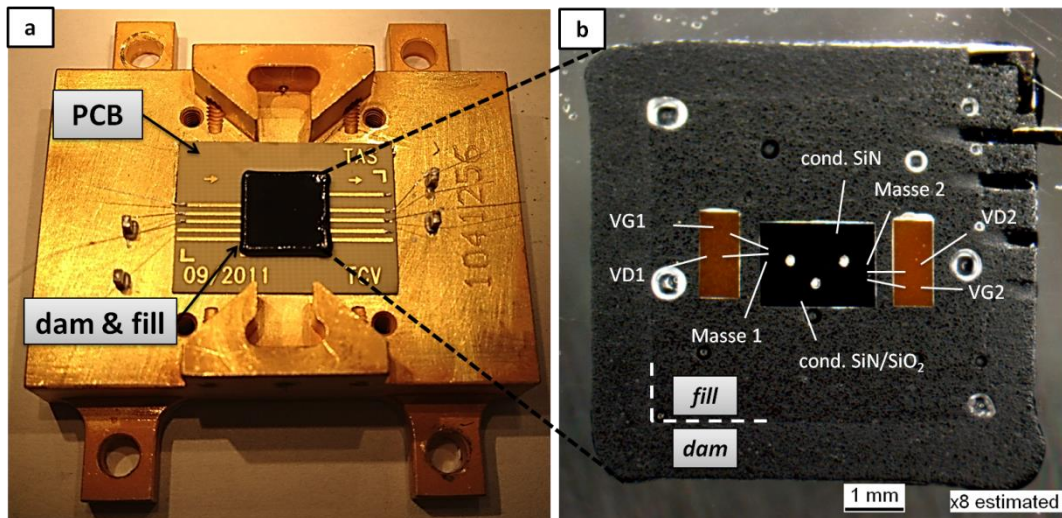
a - Vue en optique d'une partie du véhicule de test avant décollement du PCB par chauffage à 200°C.
